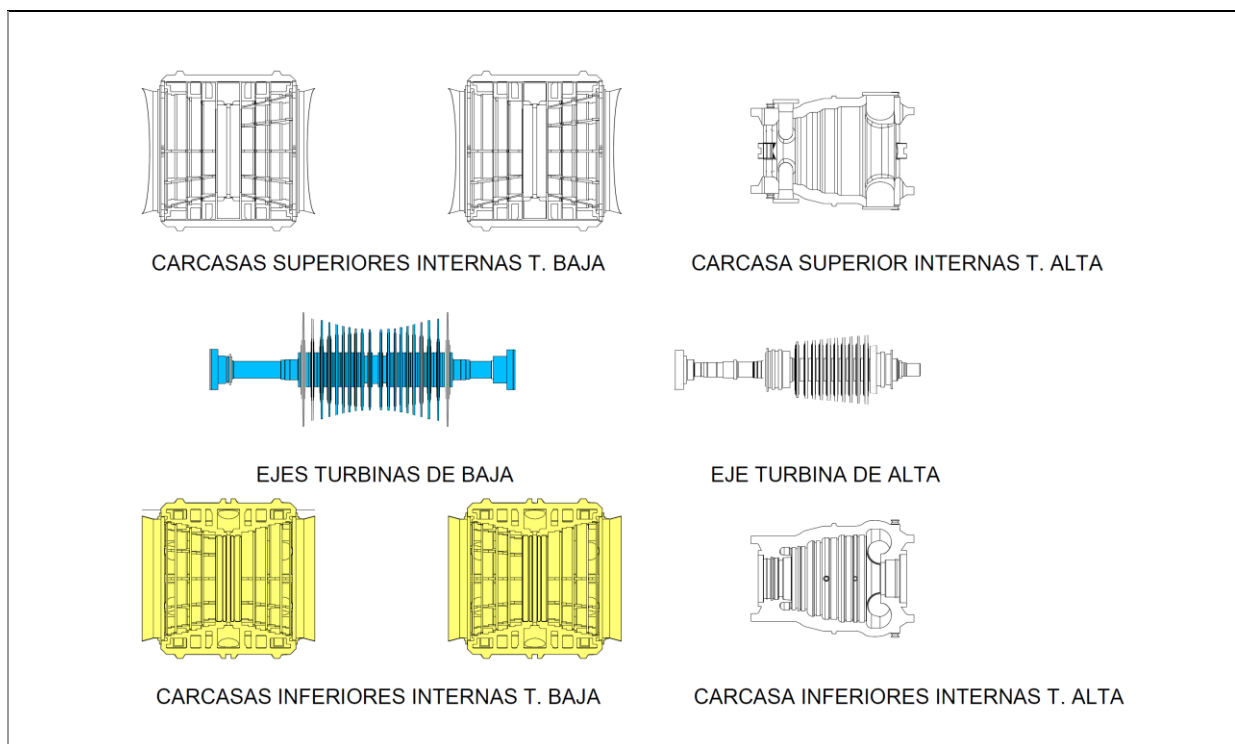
Vista de planta de piezas más relevantes a ser tratadas en el SAS POT.
